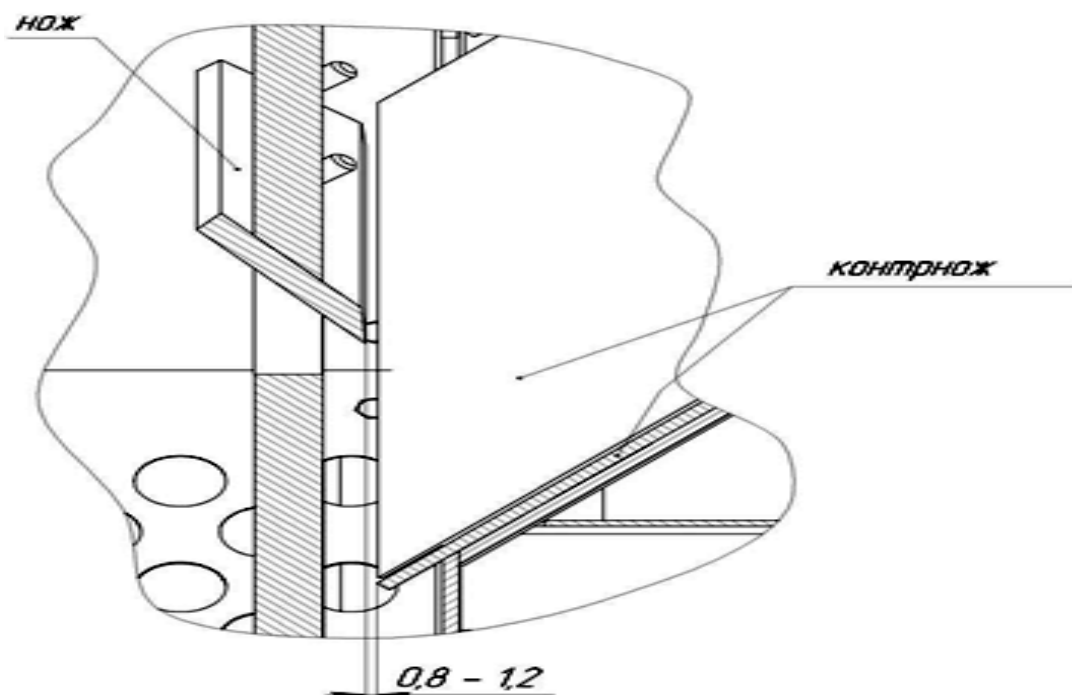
Схема регулировки зазора между ножами и контрножом
